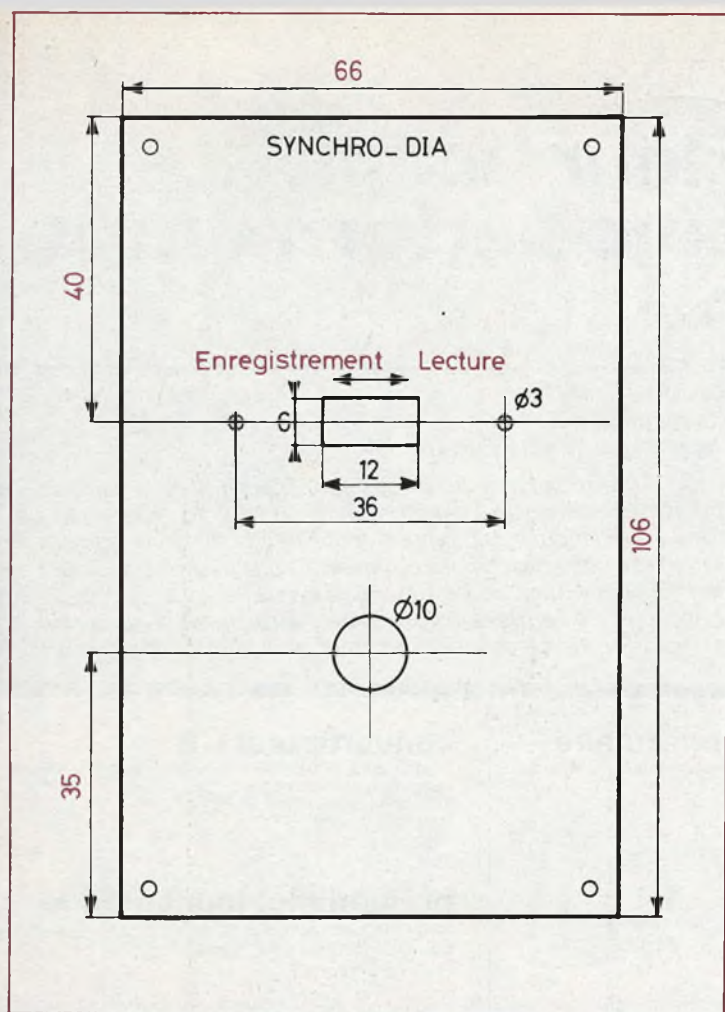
Plan de perçage de la face avant en aluminium du coffret.
